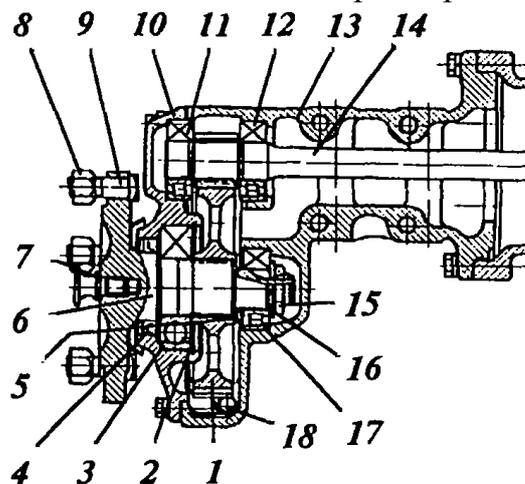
Конечные передачи: 1 - шестерня ведомая; 2 - кольцо; 3, 11, 12, 17 - подшипники; 4 - манжета; 5, 16 - шайбы; 6 - фланец; 7 - рым-болт; 8, 15 - гайки; 9 - болт; 10 - крышка; 13 - рукав;
